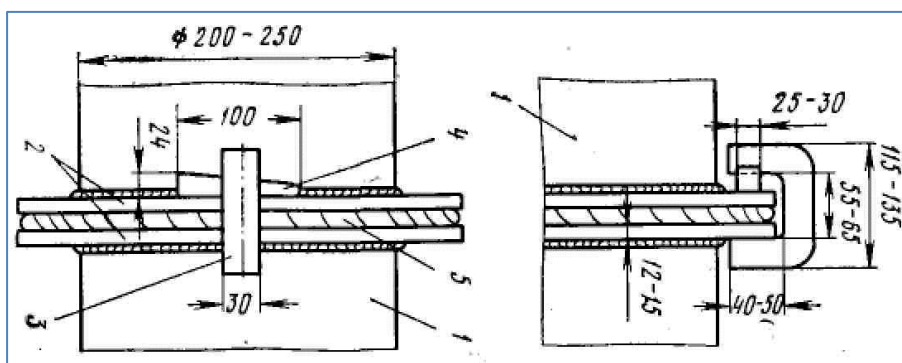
Быстроразъемное соединение забойных водоводов, применяемое на Уральских гидравлических разрезах: 1 - труба; 2 - фланцы соединяемых труб; 3 - скоба; 4 — клин; 5 - прокладка
